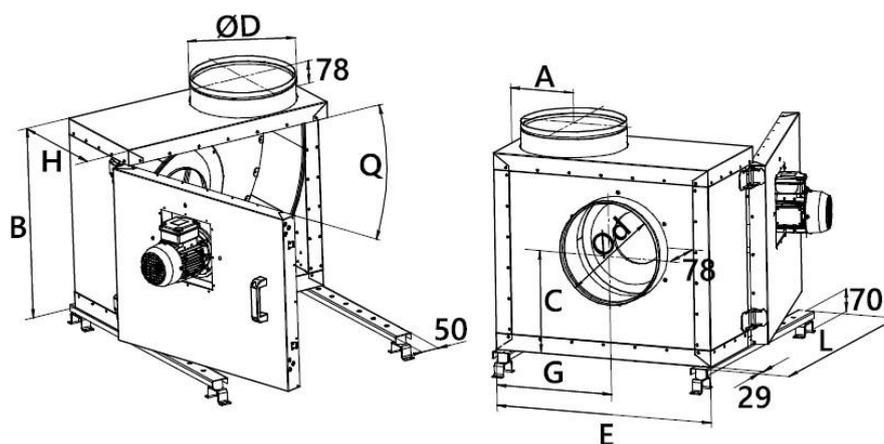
Габаритные установочные и присоединительные размеры вентиляторов
